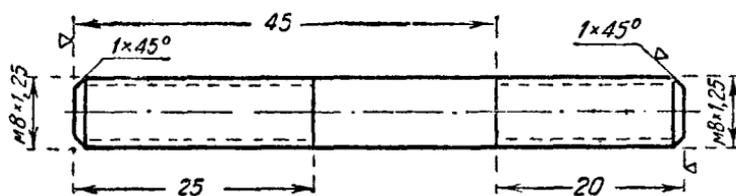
Дет. 07-62. Шпилька крышки маслоприёмника
